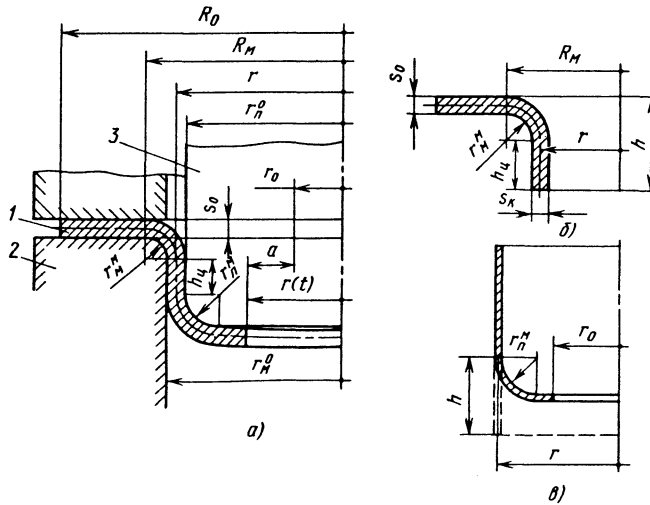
Получение борта вокруг круглого отверстия: а - формообразование; б - развернувшийся борт; в - борт в дне цилиндрической оболочки; 1 - заготовка; 2 - матрица; 3 - пуансон
